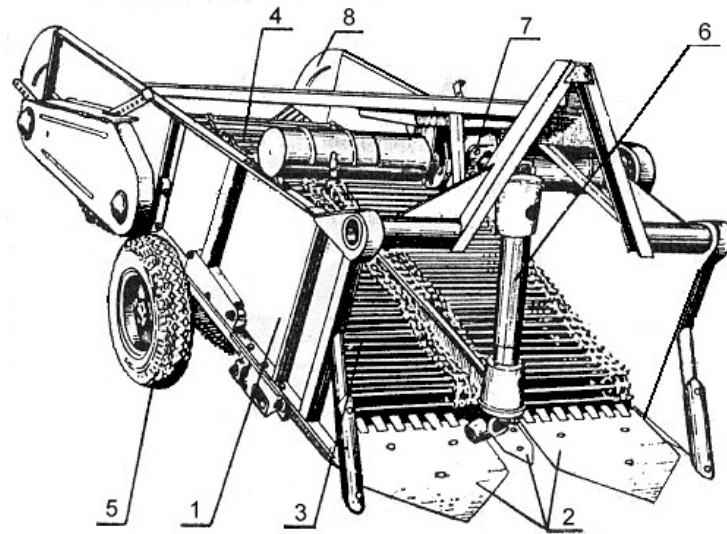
Картоплекопач КТН-2В: 1 – рама; 2 – лемеші; 3 – основний елеватор; 4 – каскадний елеватор; 5 – колесо опорне; 6 – передача карданна; 7 – редуктор; 8 – відбивач
